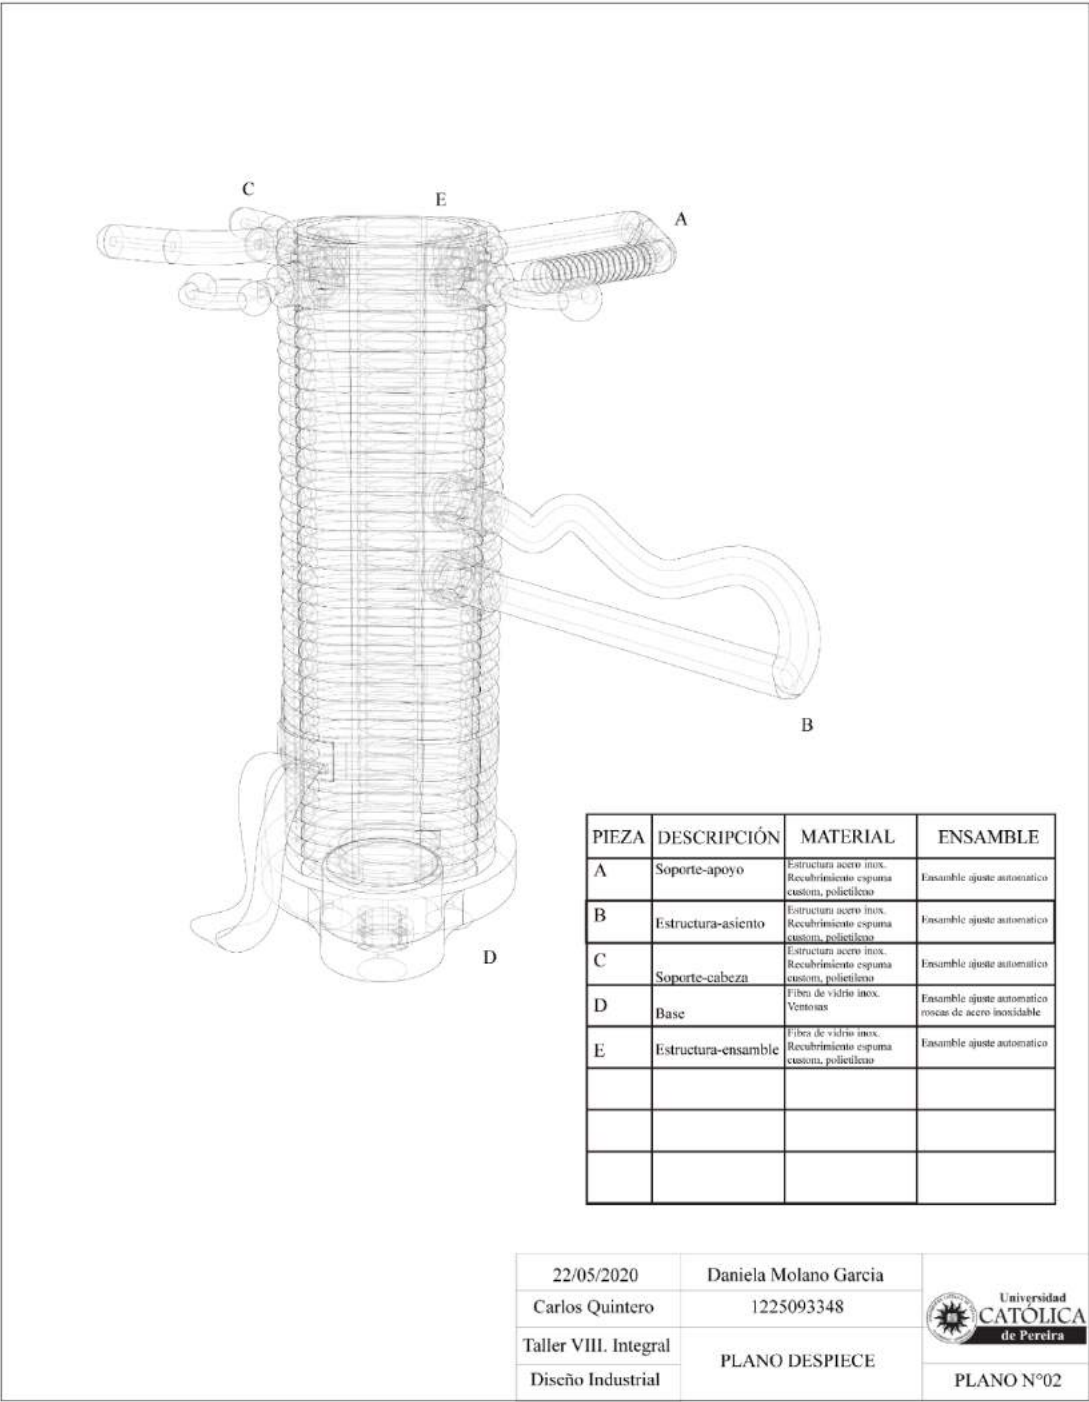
Planos técnicos, despiece. Fuente: Elaboración propia.
